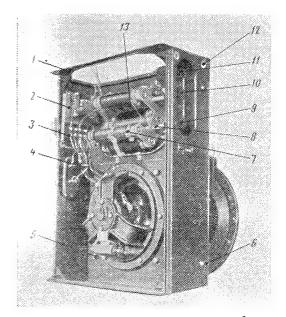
Блок аппаратуры: 1 — корпус; 2 — осветительный трансформатор; 3 — зажимы для присоединения проводов; 4 — держатель предохранителя; 5 — болт для крепления кожуха; 7 — блок сопротивлений; 8 — поводок; 9 — колпачок, закрывающий ручку реостата регулировки компаундирующего сопротивления; 10 — ручка реостата регулировки напряжения; 11 — кнопка возбуждения; 12 — отверстие для крепления блока приборов; 13 — каретка с контактными пружинами
